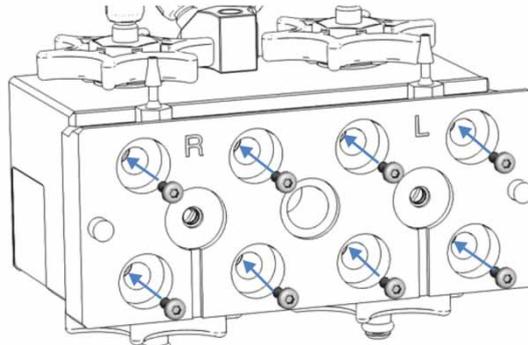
Pumpenkopf mit Hinterspülplatte und Schrauben für die Platte
